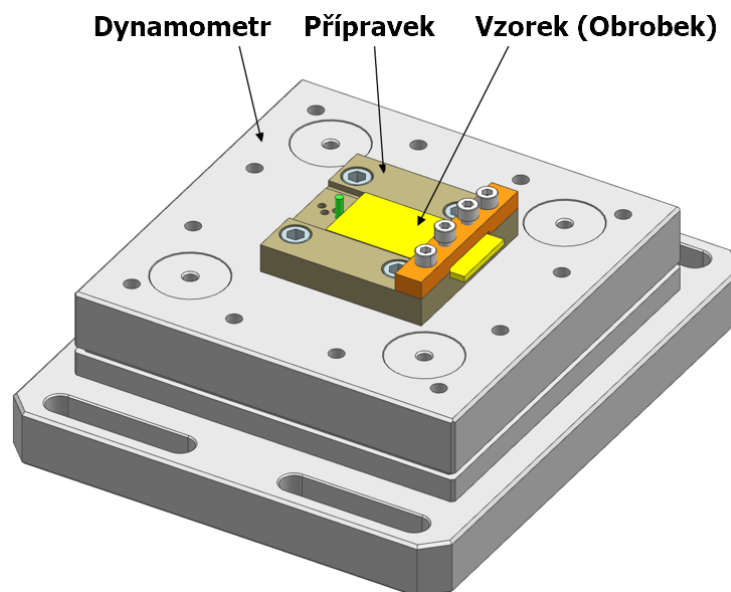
Sestava pro měření sil při realizovaných experimentech při frézování.
